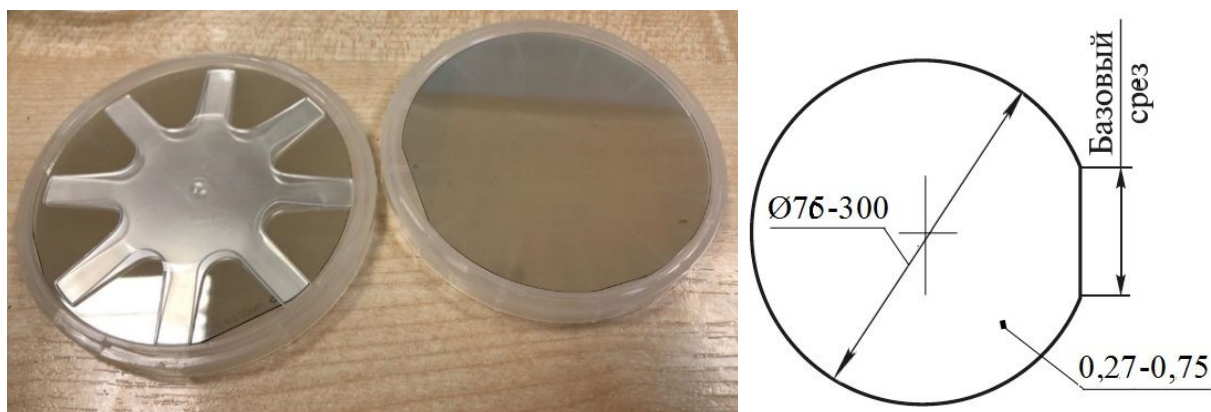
Внешний вид (слева) и эскиз (справа) карбидокремниевых пластин
